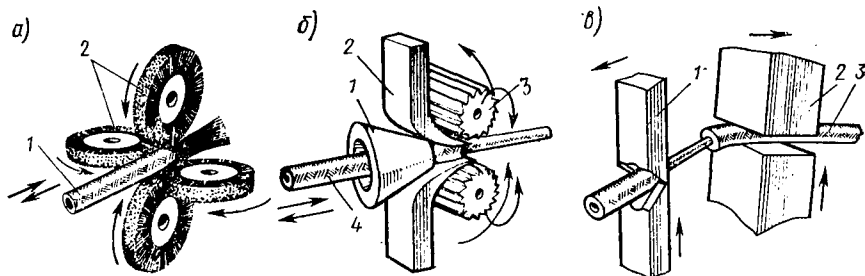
Схемы установок для расчесывания экрана, кабеля, снятия экранирующей оплетки и изоляции с проводов
